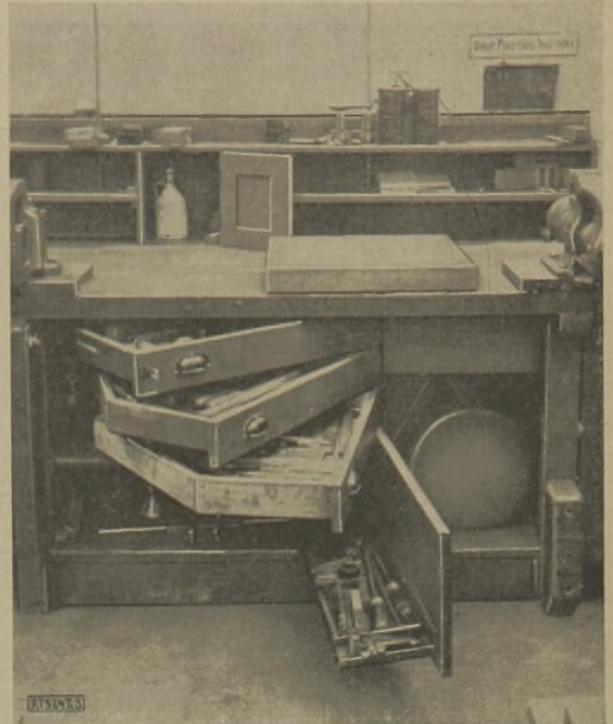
Feilbank mit ausschwenkbaren Werkzeugkästen. Siemens-Schuckertwerke A.-G.
